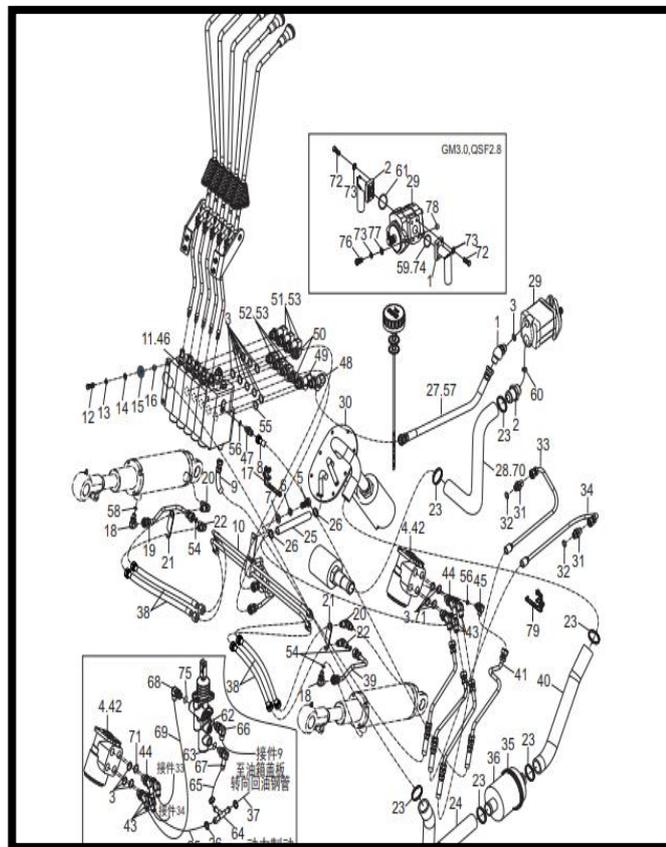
Elementos del sistema hidráulico de montacargas (Heli, 2019)
